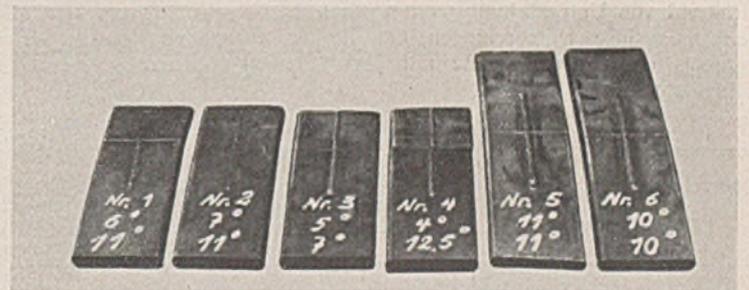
Biegeprobe mit aufgeschweißter Längsraupe (nach Kommerell).
